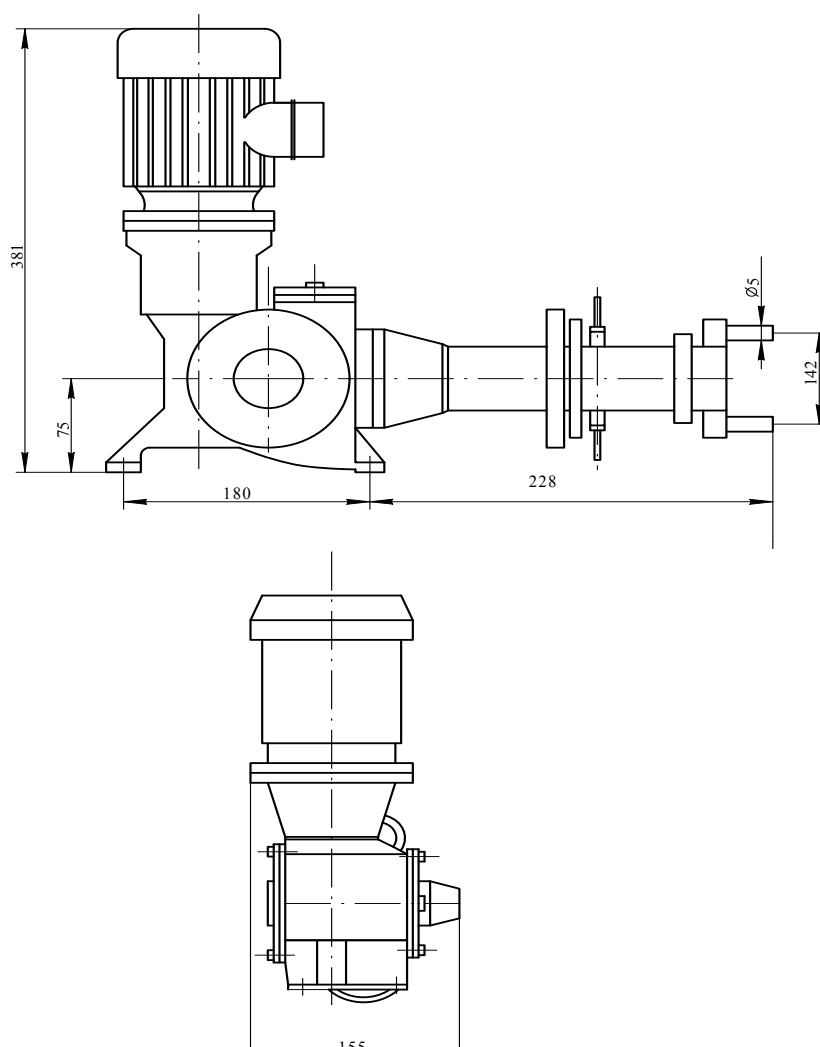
Габаритный чертеж насоса - дозатора подачи ацетата цинка
